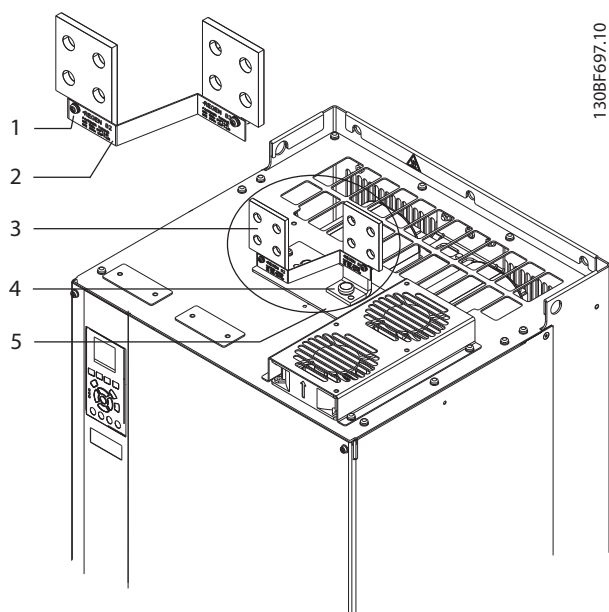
Montando a placa para acesso de cabos e a tampa de terminal
